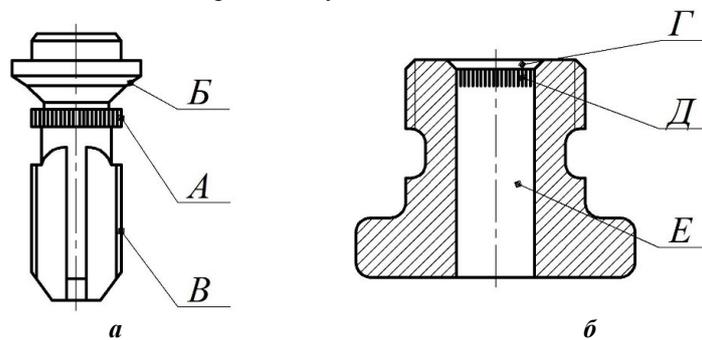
Места износа рабочих поверхностей нагнетательного клапана: а – клапан; б – седло; А – разгрузочный пояс; Б – запирающий конус; В – направляющий хвостовик; Г – фаска седла; Д – поверхность, сопрягающаяся с пояском; Е – направляющее отверстие.
